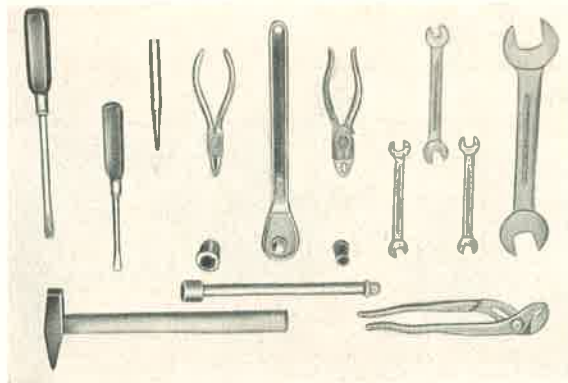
Zusammenstellung der Werkzeuge, die für die Arbeit Gr. MA Motoraufhängung gebraucht werden.
